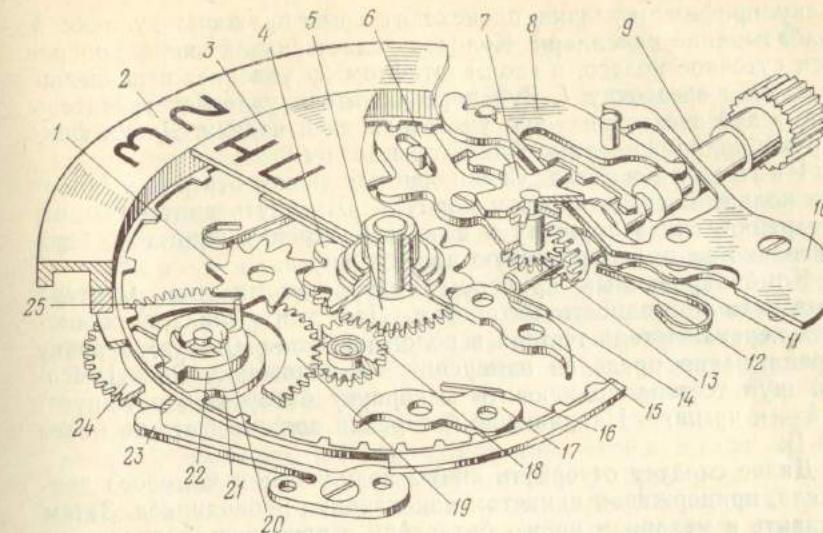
Кинематическая схема календарного устройства кварцевых часов 3050:
